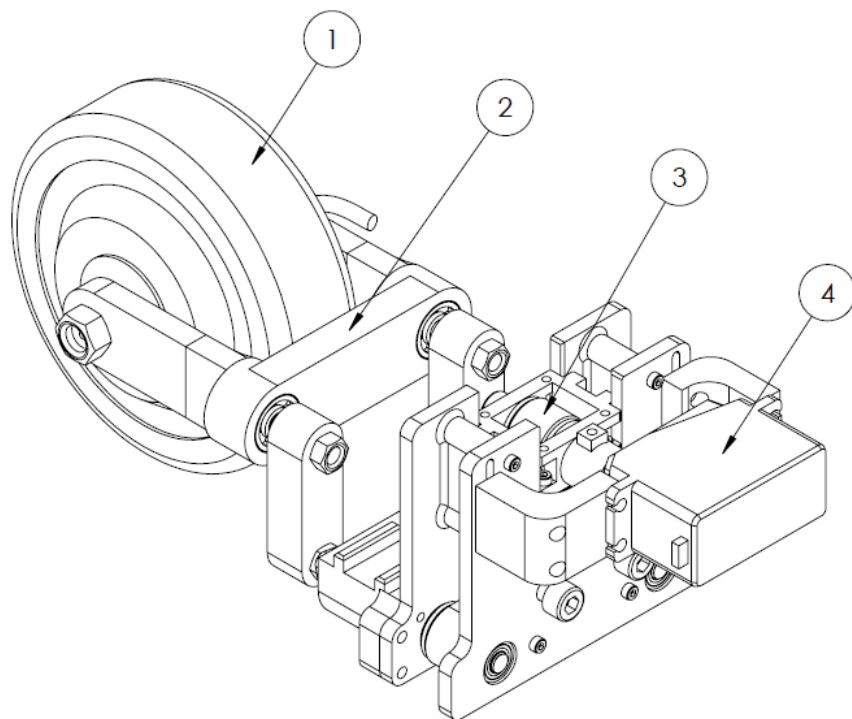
Механізм стабілізації пристрою: 1) заднє мотор-колесо; 2) кріплення колеса; 3) пасова передача із зубчатим пасом; 4) сервопривод
